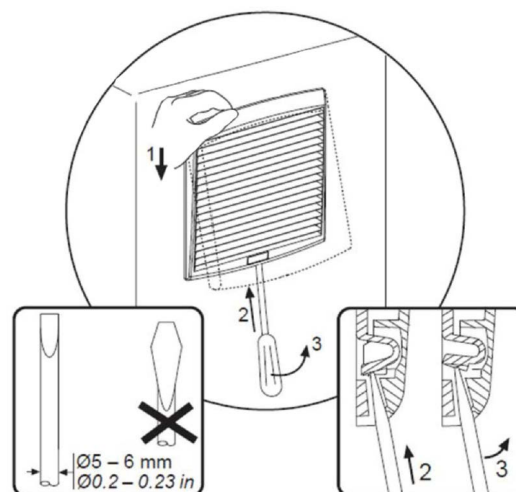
ouvrir le module de motorisation (PDM) pour remplacer l'élément de filtre.
